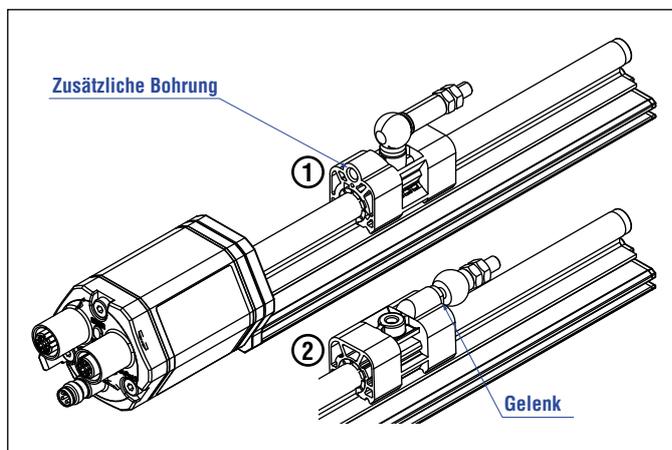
Magnetausrichtung mit Magnetschlitten für RP5 POWERLINK mit interner Linearisierung
